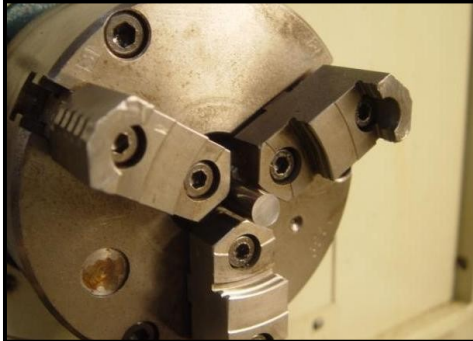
Detalhe do tarugo preso a castanha do torno antes da usinagem
